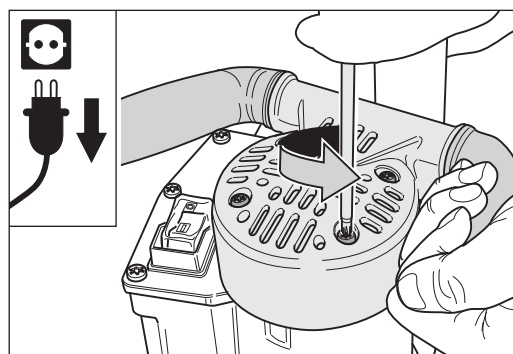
Die vier Befestigungsschrauben des Griffstücks entfernen.
